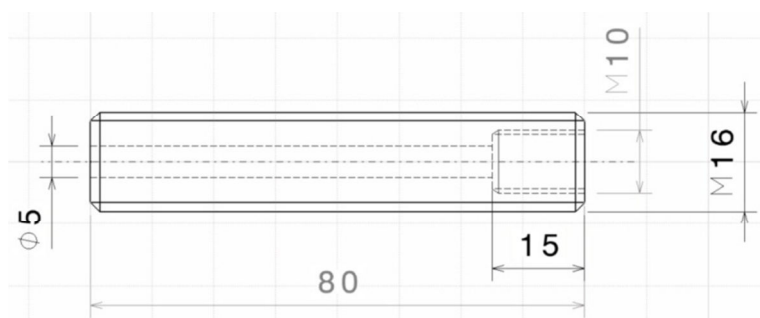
Desenho técnico da extensão para o sensor de nível.
